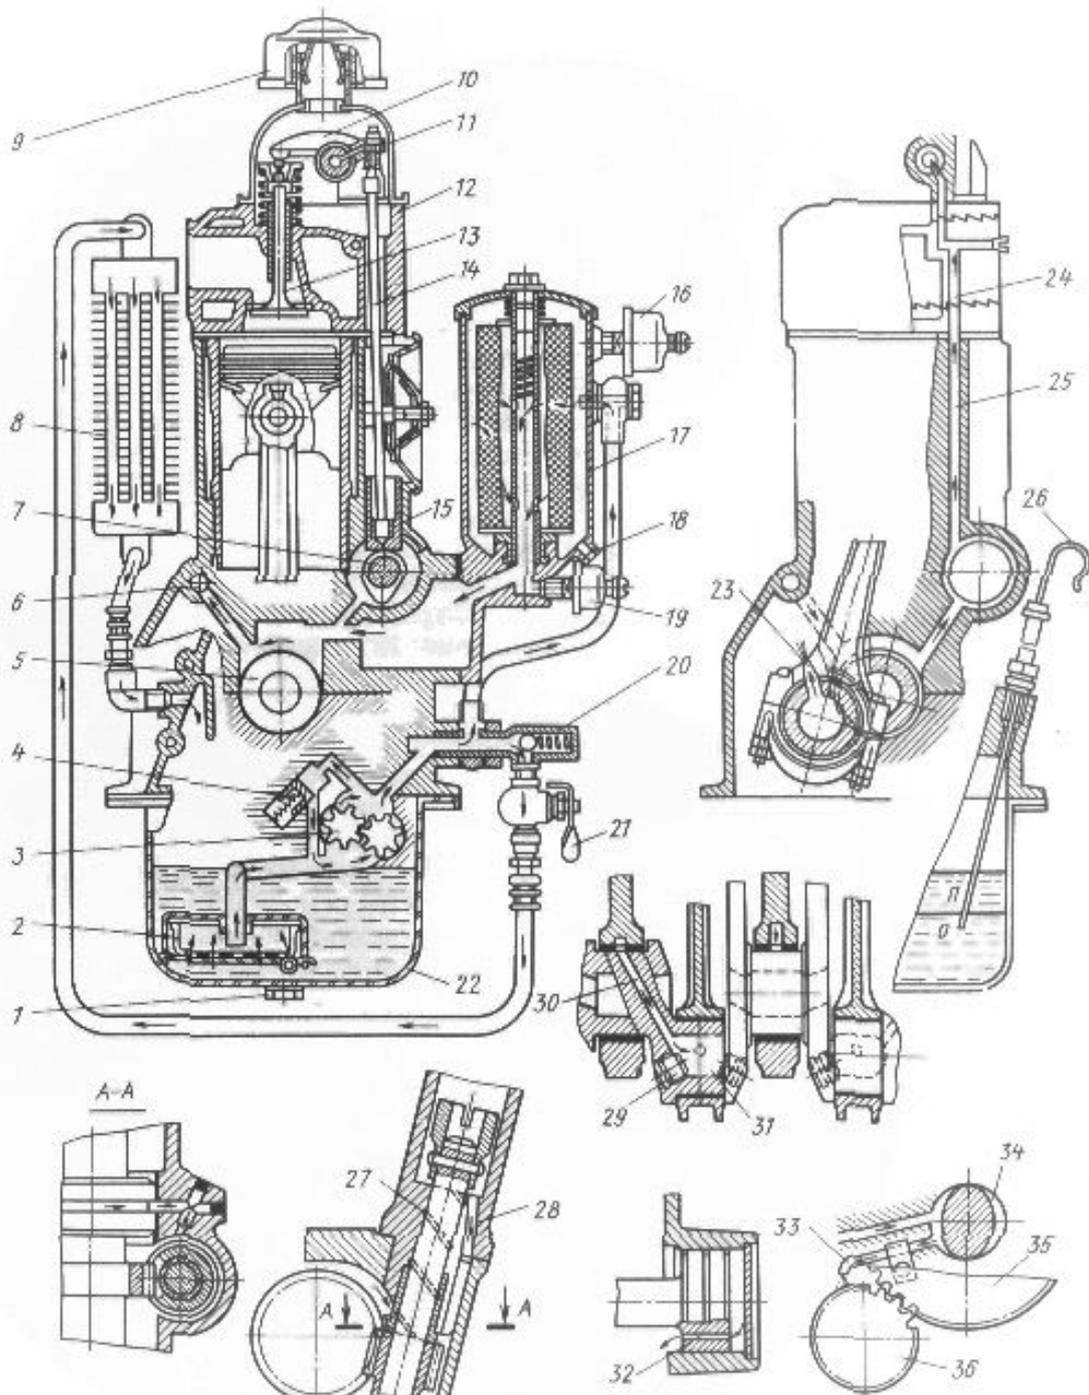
Схема смазочной системы двигателя автомобиля ГАЗ-24 «Волга»
